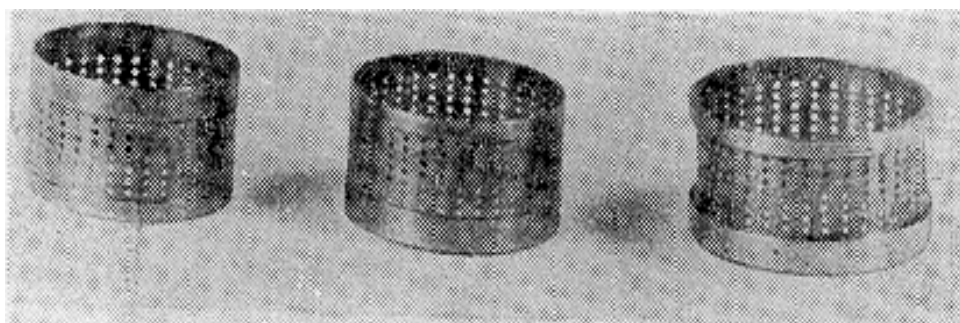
Образцы деталей, изготовленных электродом-проволокой.
